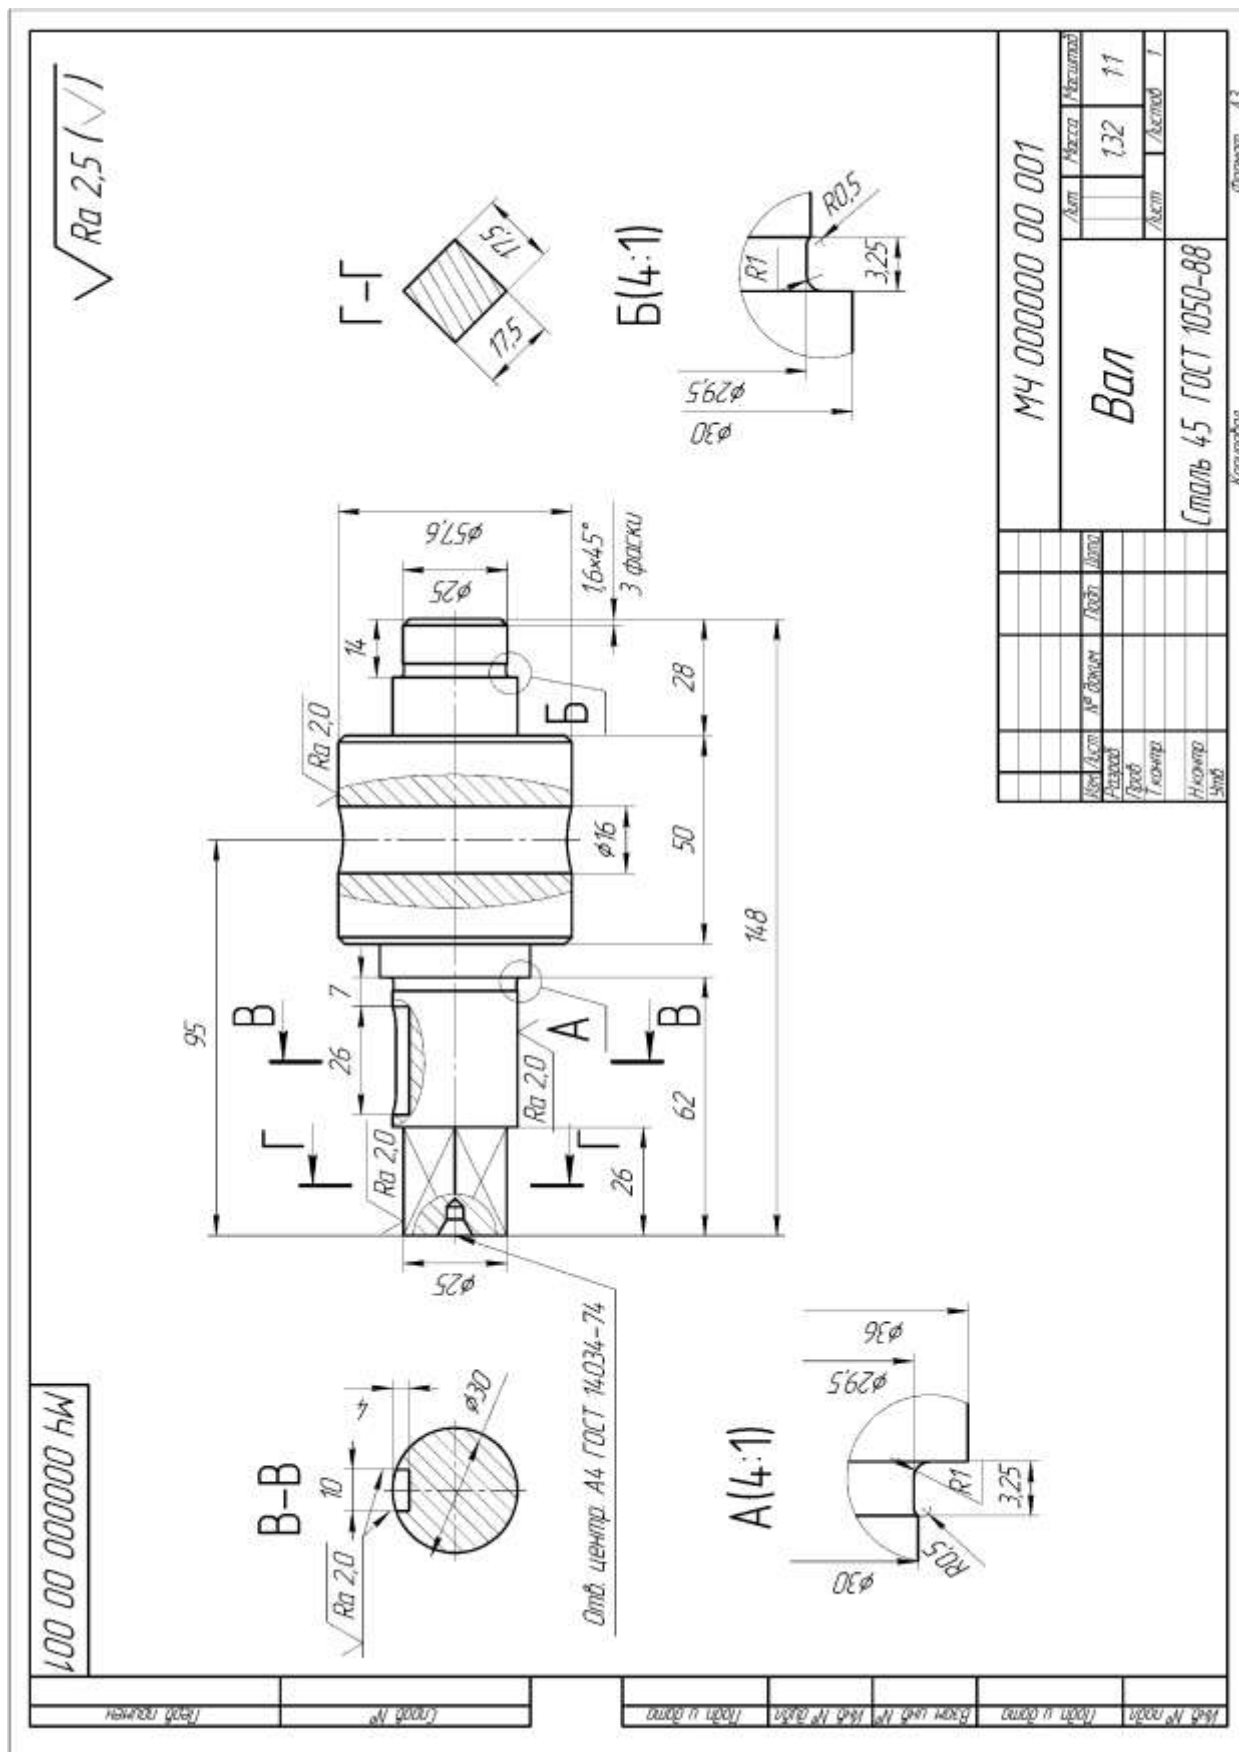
Ассоциативный чертеж вала со сквозным отверстием
